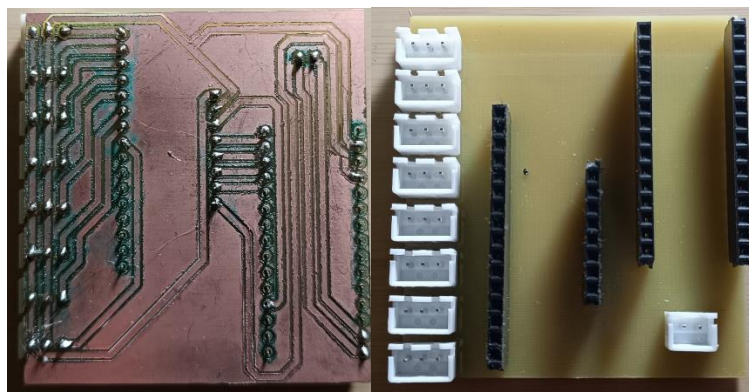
2 Imagen de la PCB con conectores JST y Pin Socket Guante
